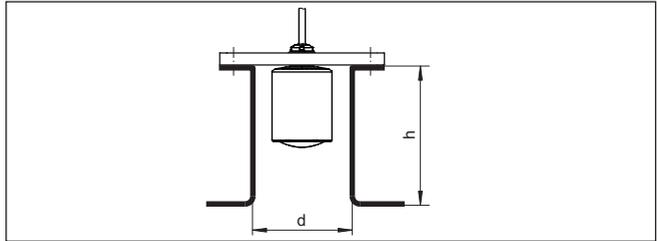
Montage de la rehausse en cas de dimensions de rehausse différente
